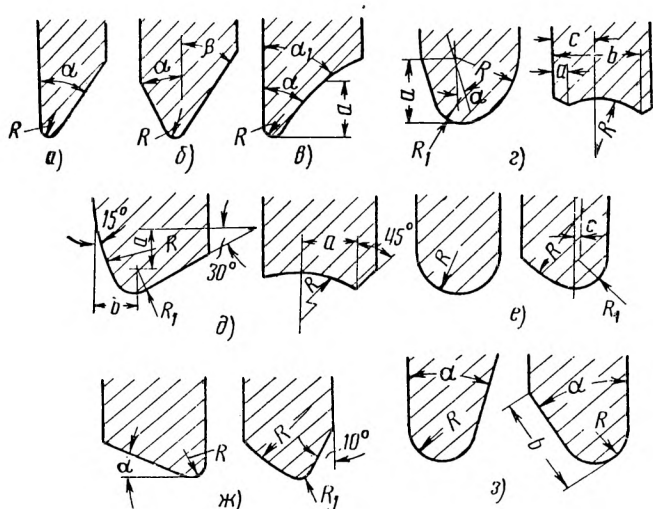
Профили фрез для фрезерования зубьев инструмента:
